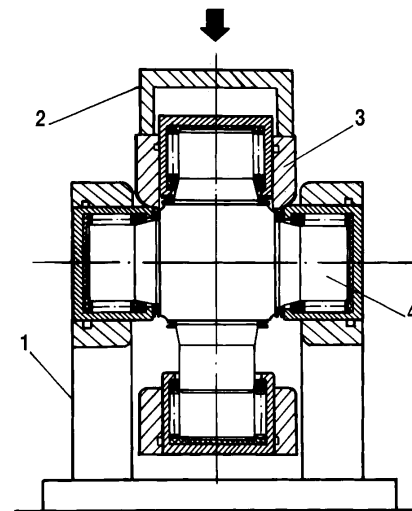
Auseinandernehmen des Kreuzgelenks:
